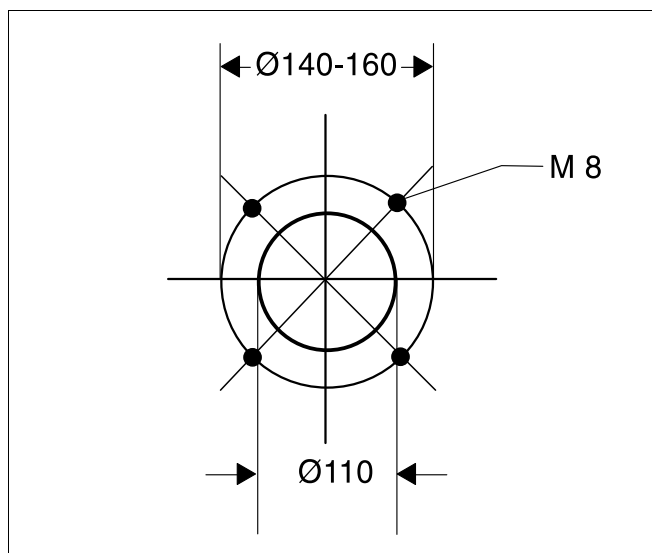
Bride de raccordement du brûleur (dim. en mm)
